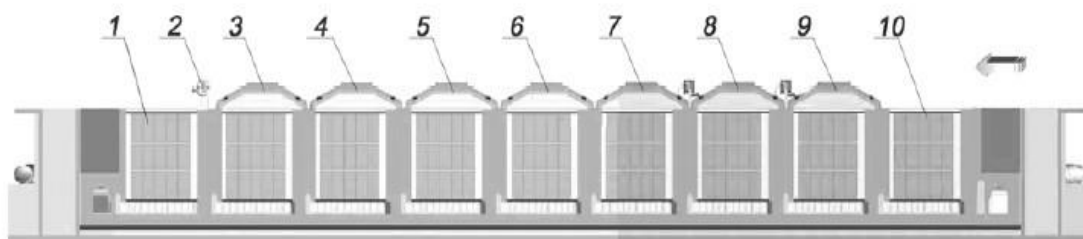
Схема випалювання заготовок у багатокамерній закритій печі типу
